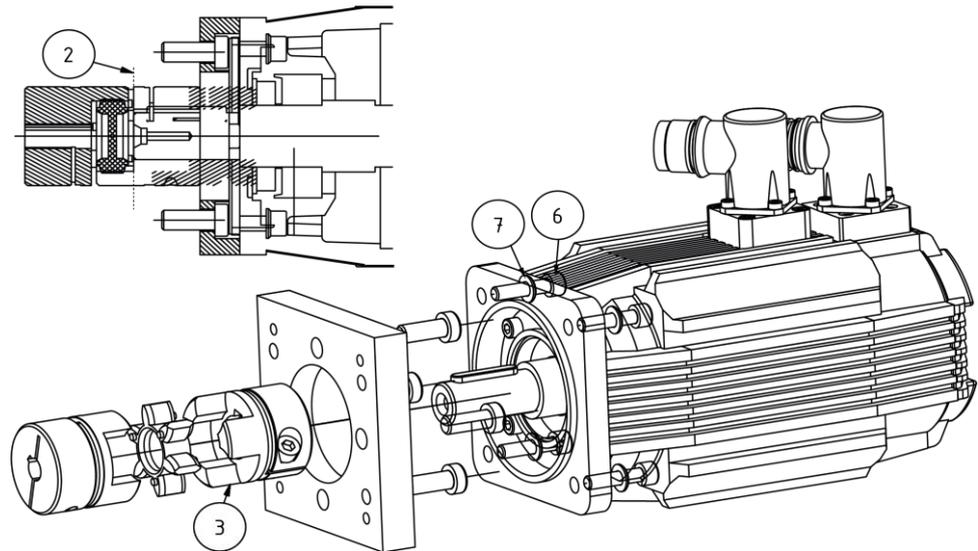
Motor-/Getriebemontage ETH032 ... ETH080 inline
